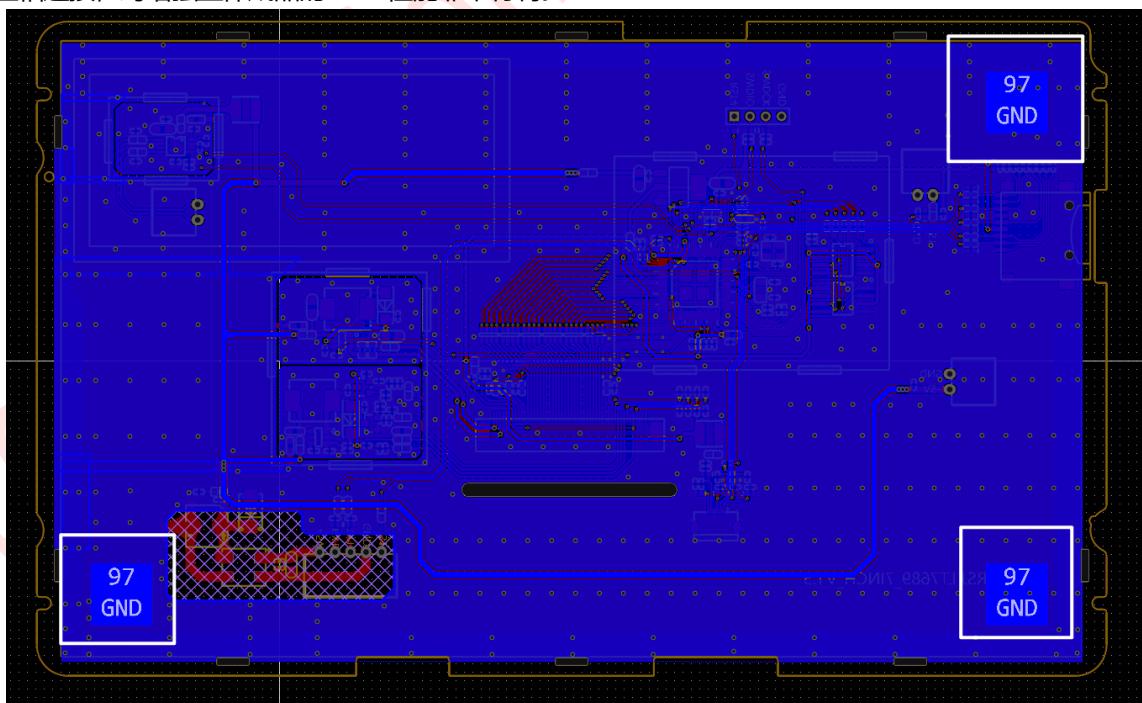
PCB 上的 GND 焊盘示意图
